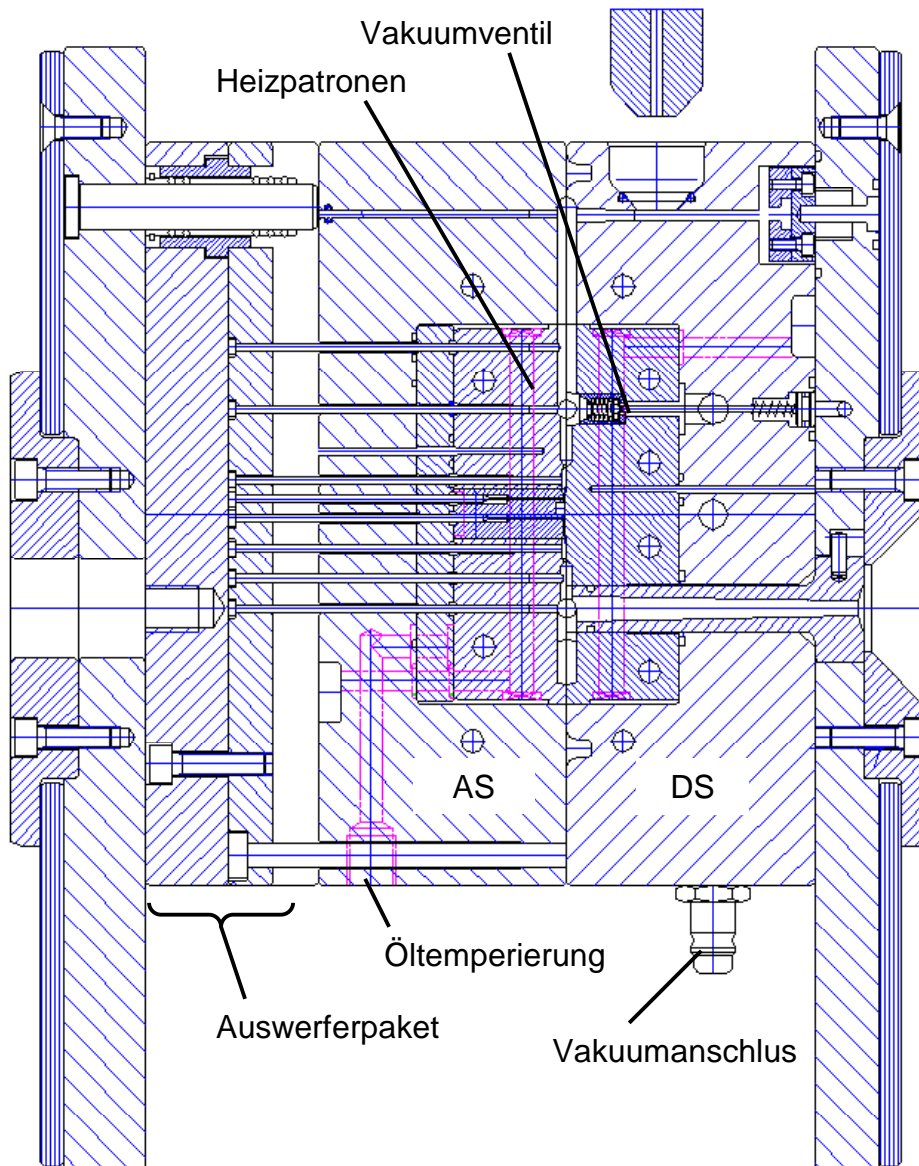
Aufsicht auf die zentrale, horizontale Schnittebene des 2K-PIM-Werkzeuges
